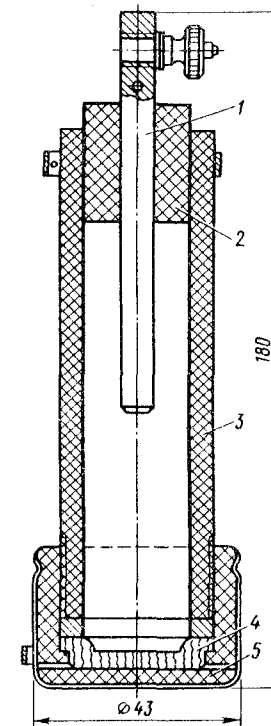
Медносульфатный неполяризующийся электрод ИМ-СЭ-58: 1 — медный электрод; 2 — корпус; 3 — пористая диафрагма; 4 — резиновая пробка; 5 — крышка защитная
